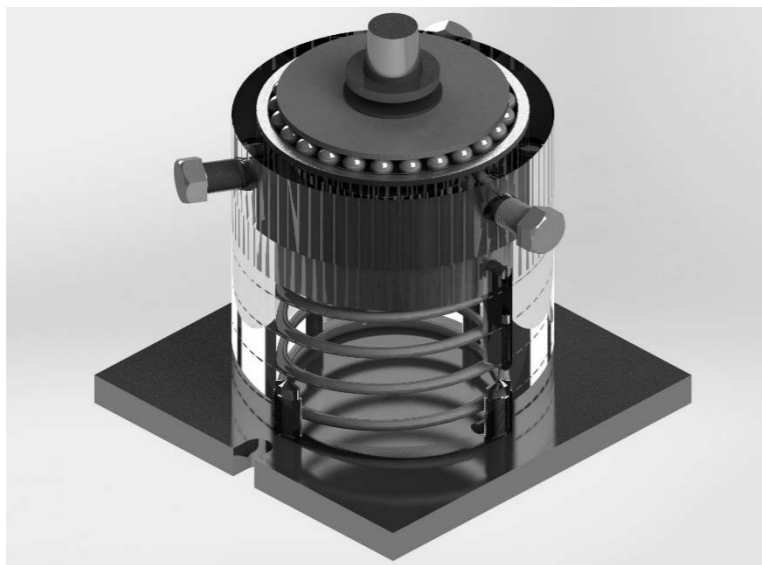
Модульная конструкция устройства для магнитно-динамического раскатывания
